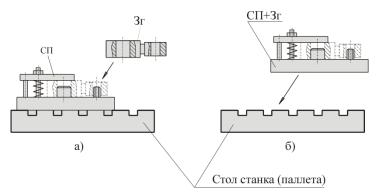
Схемы СП настольного типа: стационарного (a) и приспособления—спутники (б)
